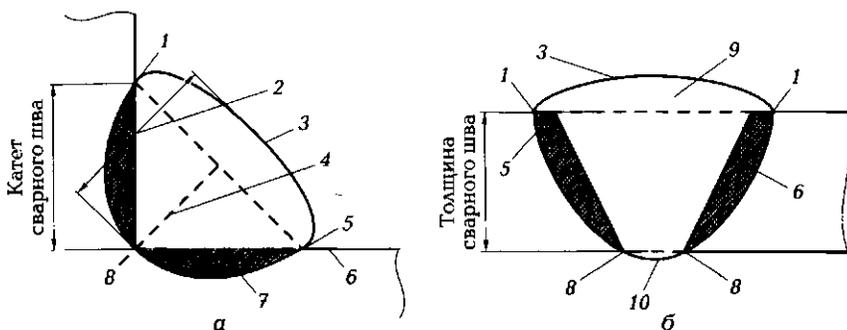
Конструктивные элементы углового (а) и стыкового (б) сварных швов:
